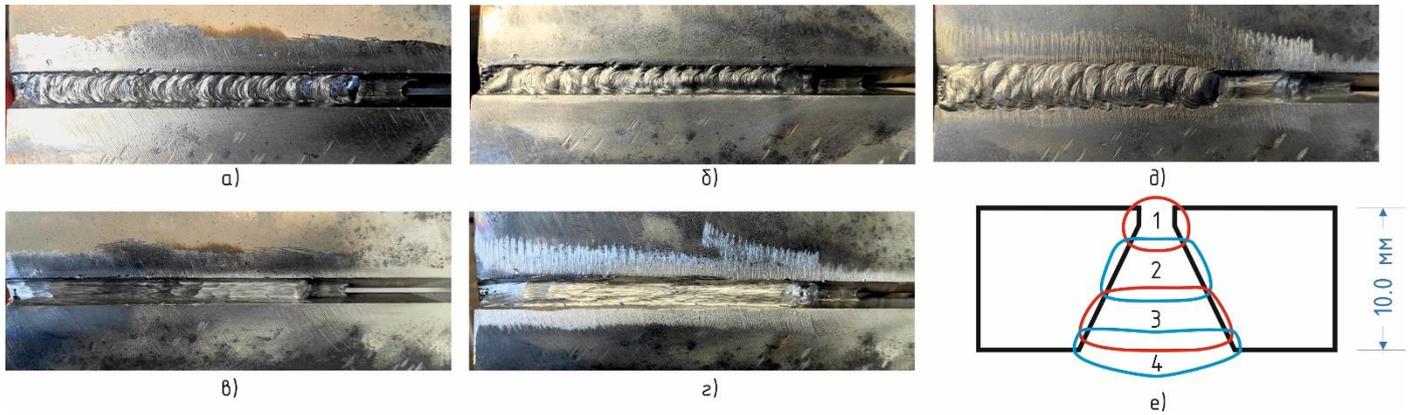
Заполнение и облицовка: а) Слой №2; б) Слой №3; в) Подготовка слоя №2; г) Подготовка слоя №3; д) облицовочный слой №4; е) Схематическое изображение соединения.
